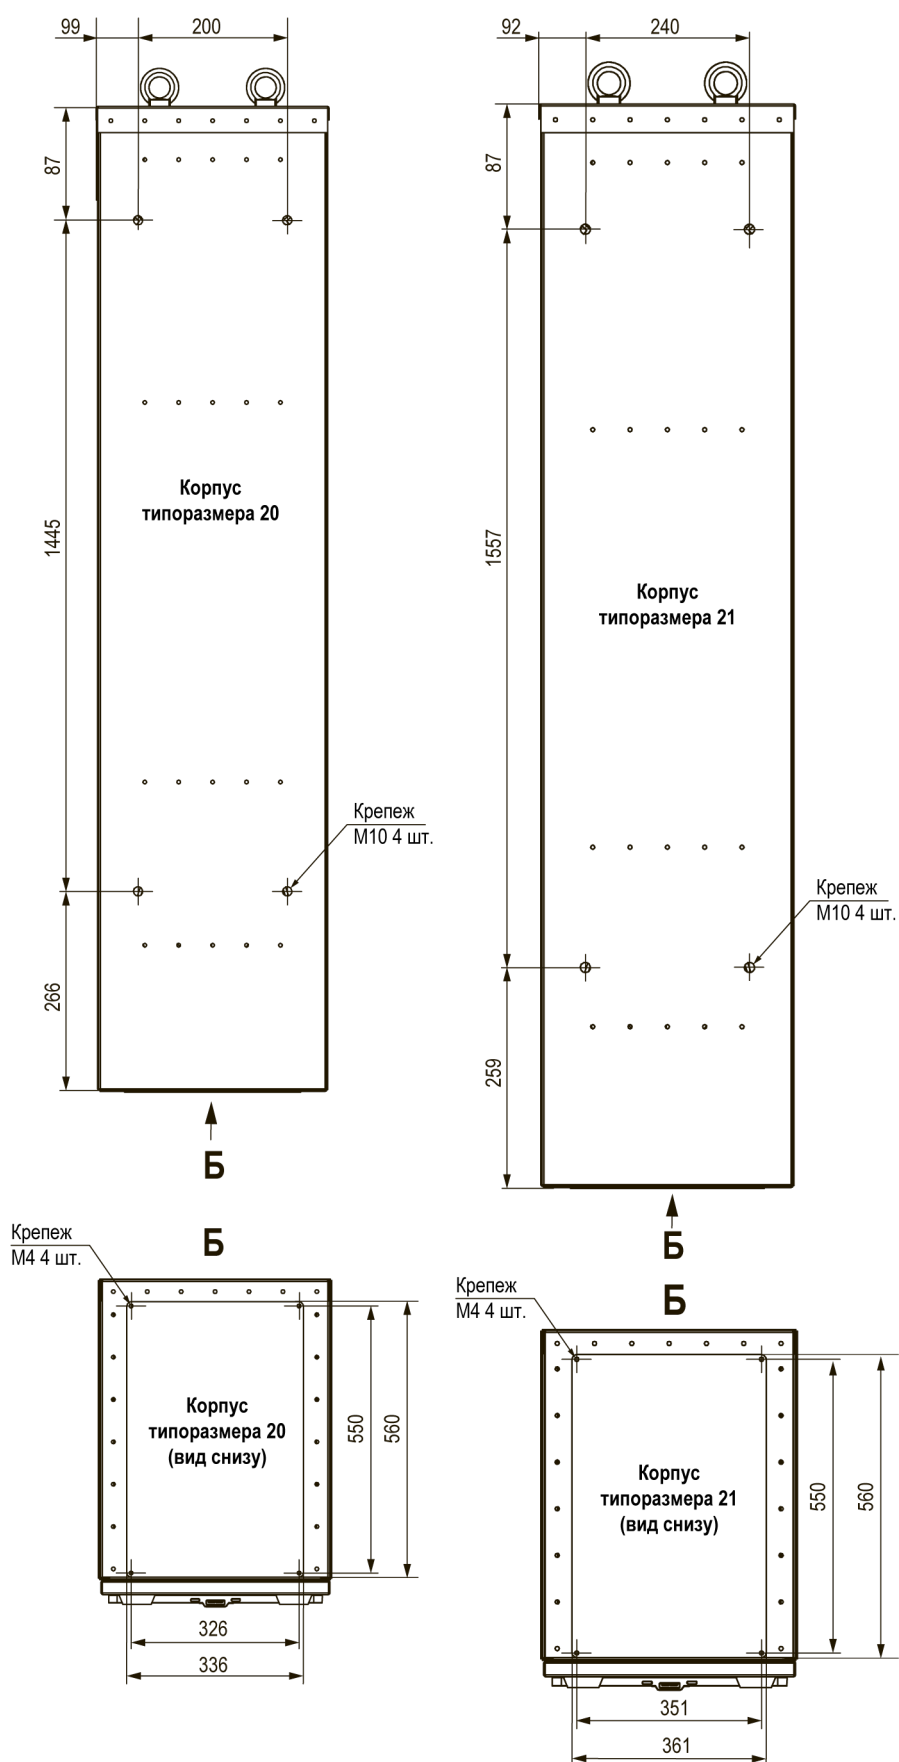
Присоединительные размеры для корпусов типоразмеров 20 и 21
